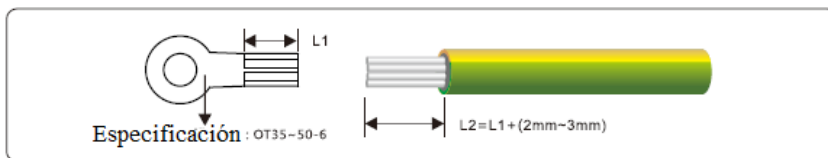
Longitud de la parte crimpada del cable (unidad: mm)
